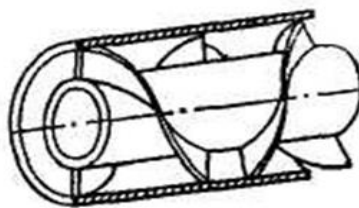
Конструктивное решение, согласно которому винтовые элементы расположены на поверхности центральной трубы либо вала кавитатора
